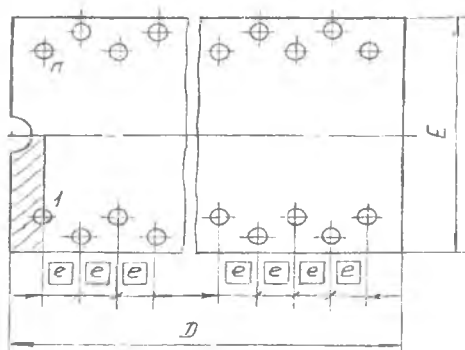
Конструкция корпуса типа 5 подтипа 1
